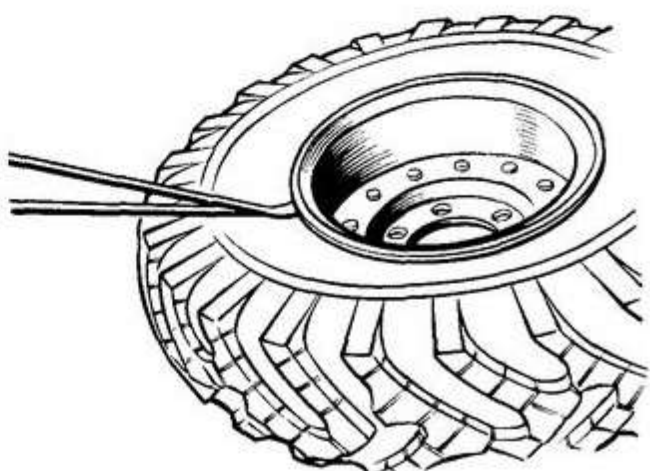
Отжатие бортового кольца шины вниз вилочной лопаткой
